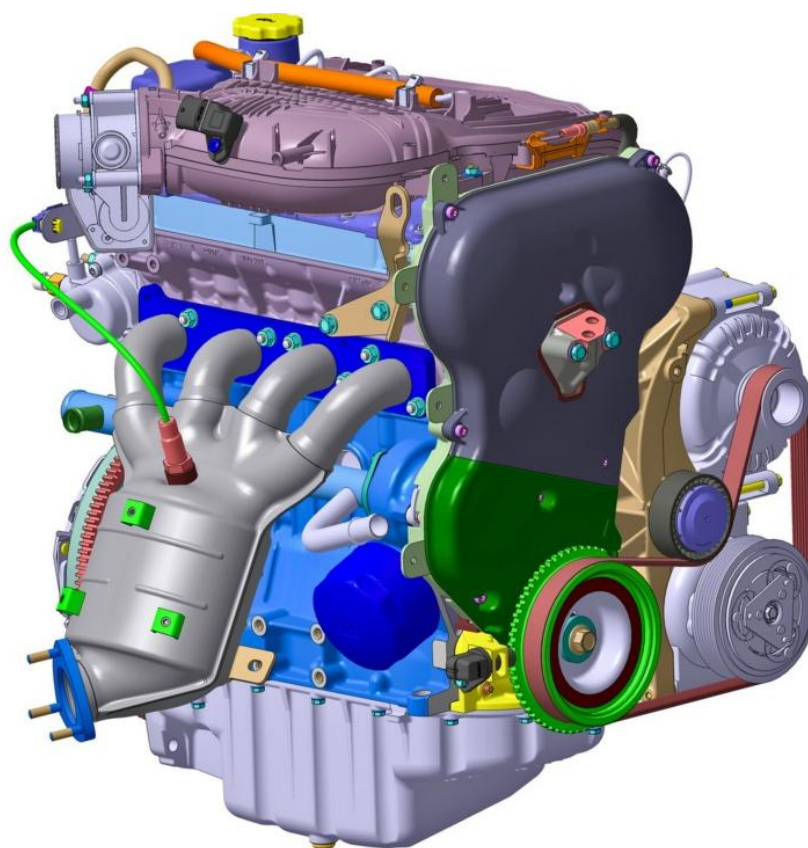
Внешний вид двигателя ВАЗ 21179
